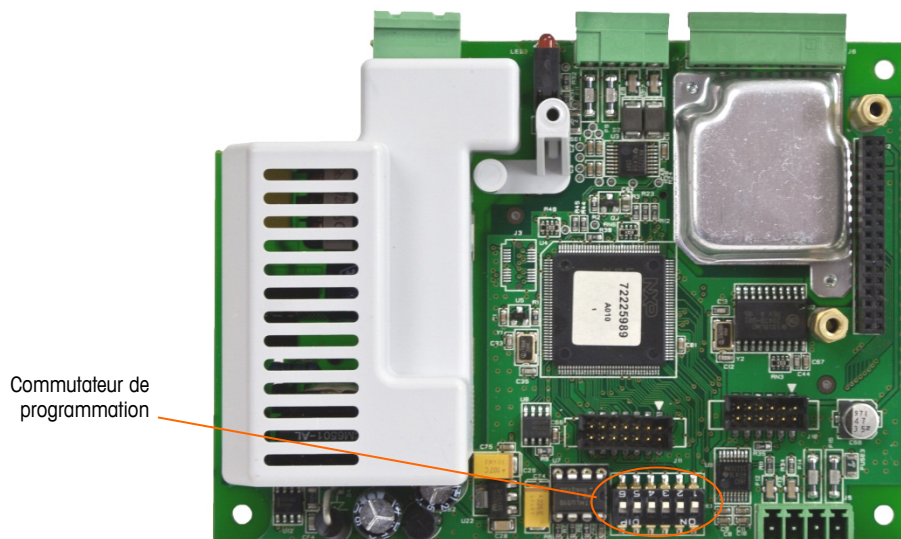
Zone de commutateurs DIP de la carte PCB principale
